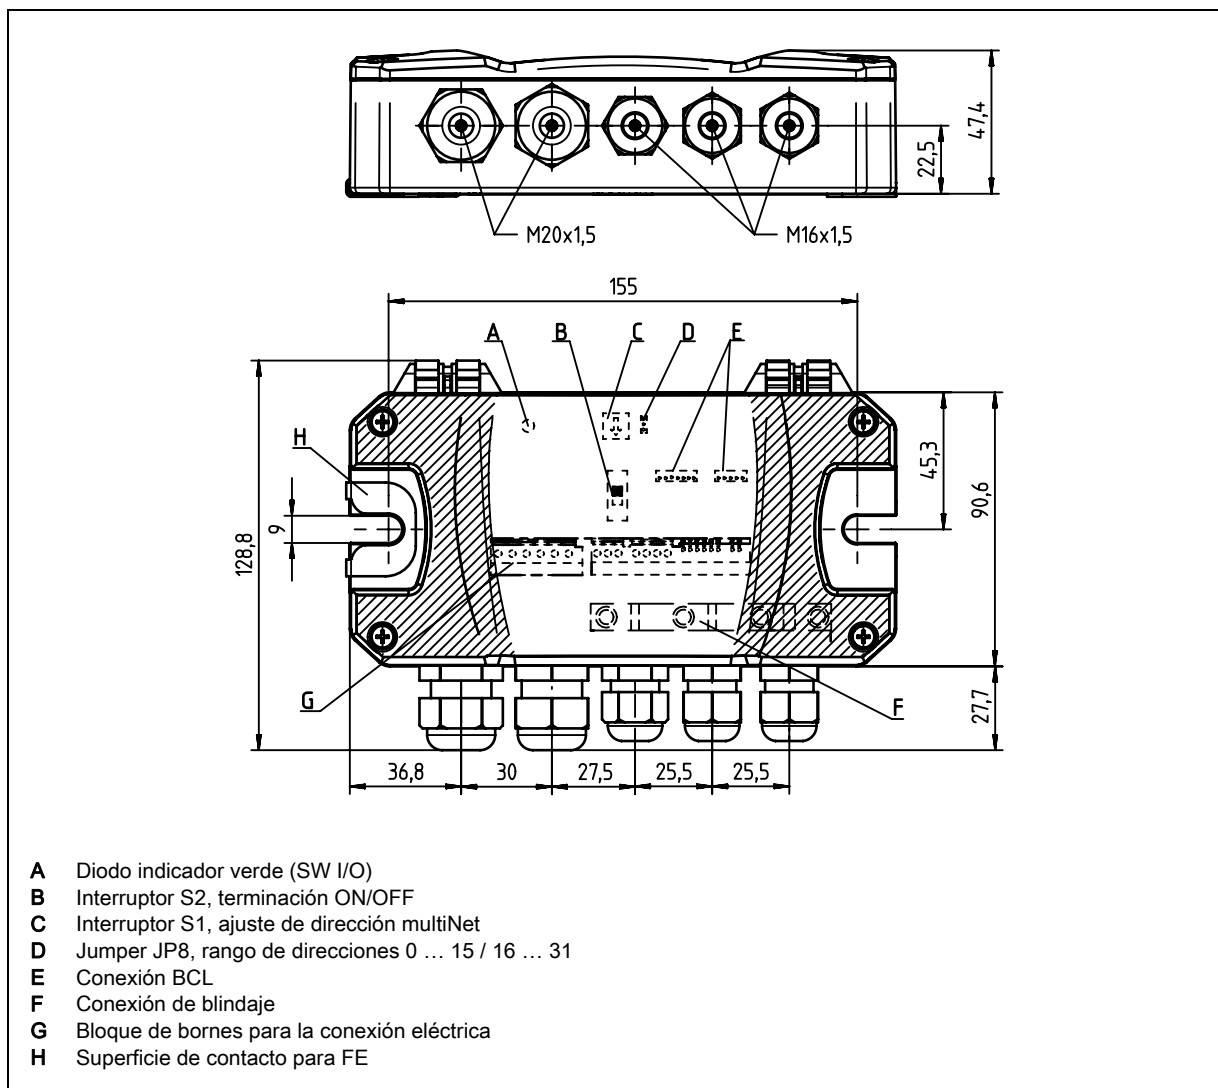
Dibujo acotado caja de bornes MA 100
